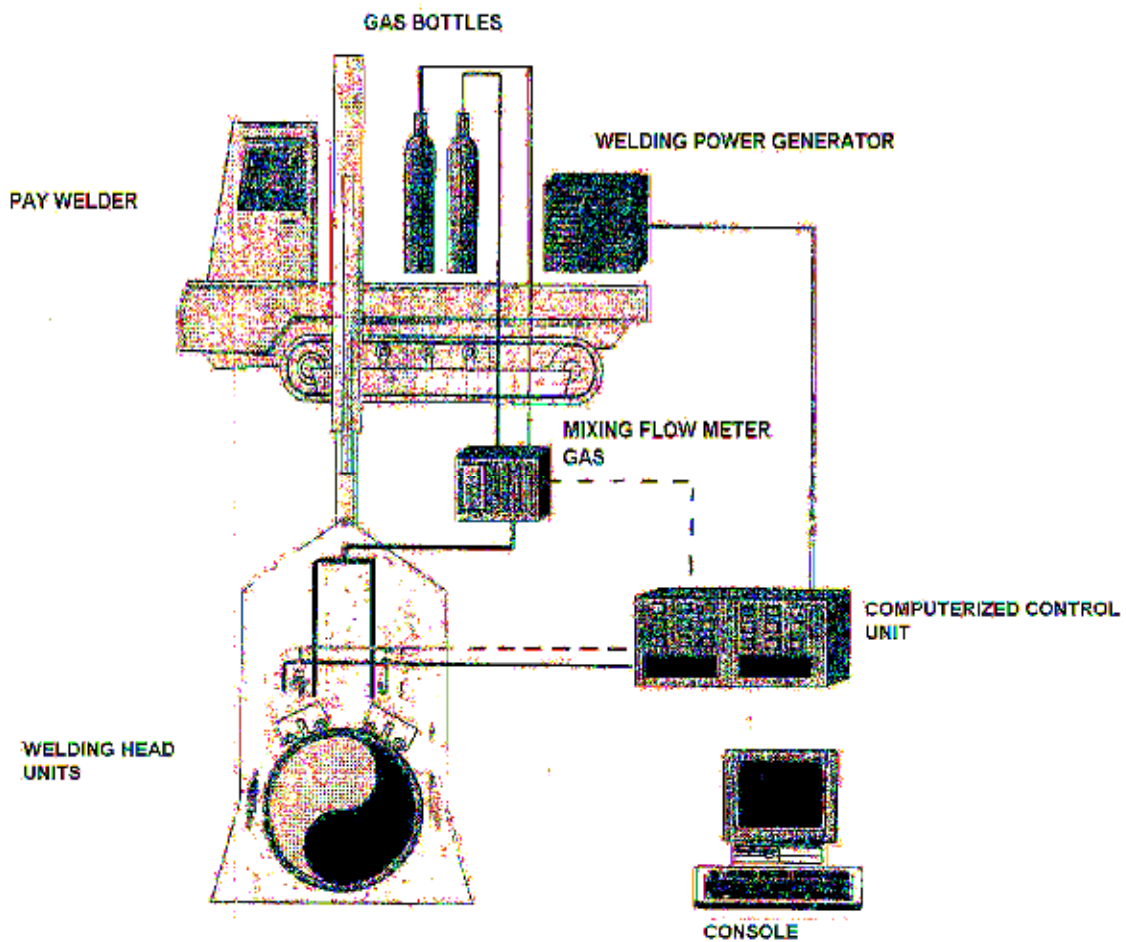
Configuración de los sistemas mecanizados de soldadura automática que serán empleados en el Proyecto.
